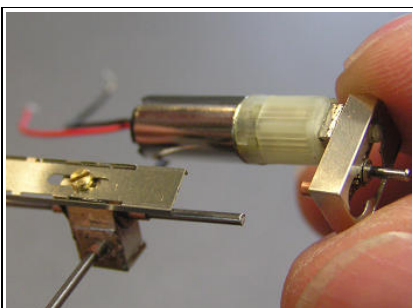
Das Getriebe wird am besten hinter der Heckachse positioniert und auf die Durchtriebswelle aufgesteckt.
